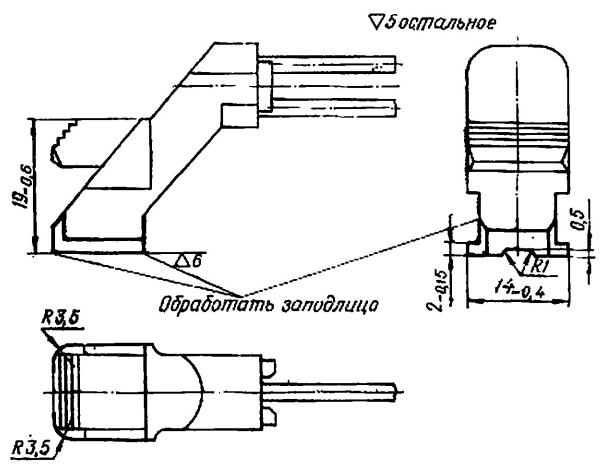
Обработка выступов пятки паправляющей возвратной пружилы после наплавки
